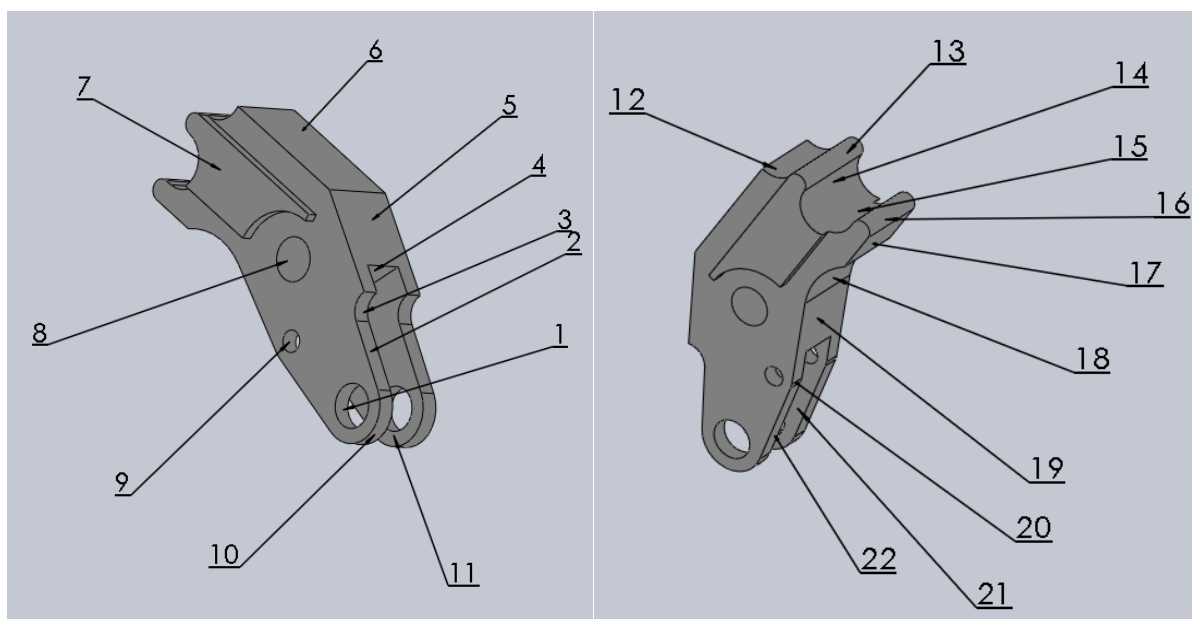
Обозначение обрабатываемых поверхностей детали
